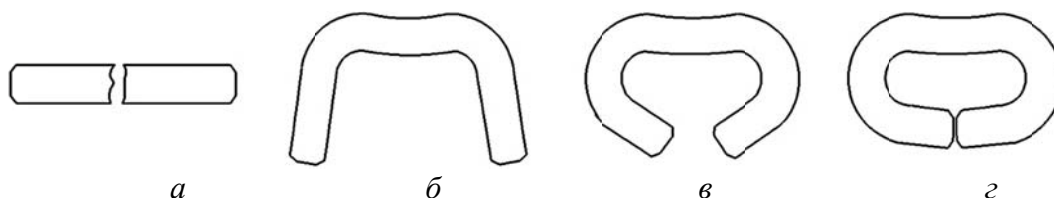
Стадии гибки прутка в заготовку звена цепи: *а* – пруток металла; *б* – полузвено; *в* – промежуточная позиция; *г* – заготовка звена
